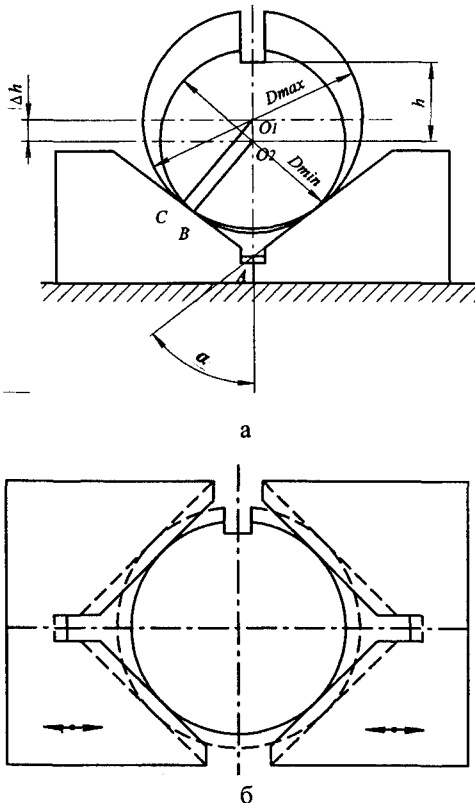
Розрахункова схема для визначення похибки установалення циліндричної деталі на призму.
